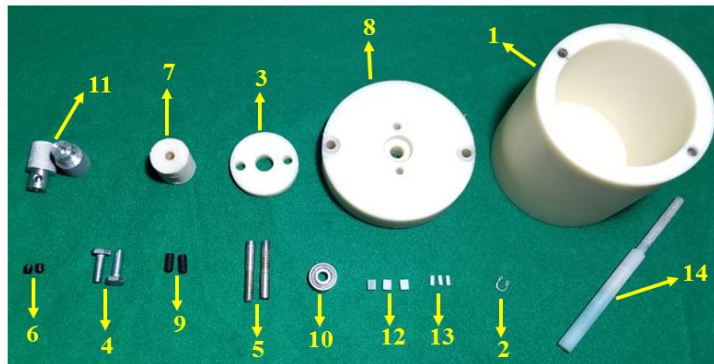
Piezas del Mezclador de Paletas inclinadas maquinadas.
